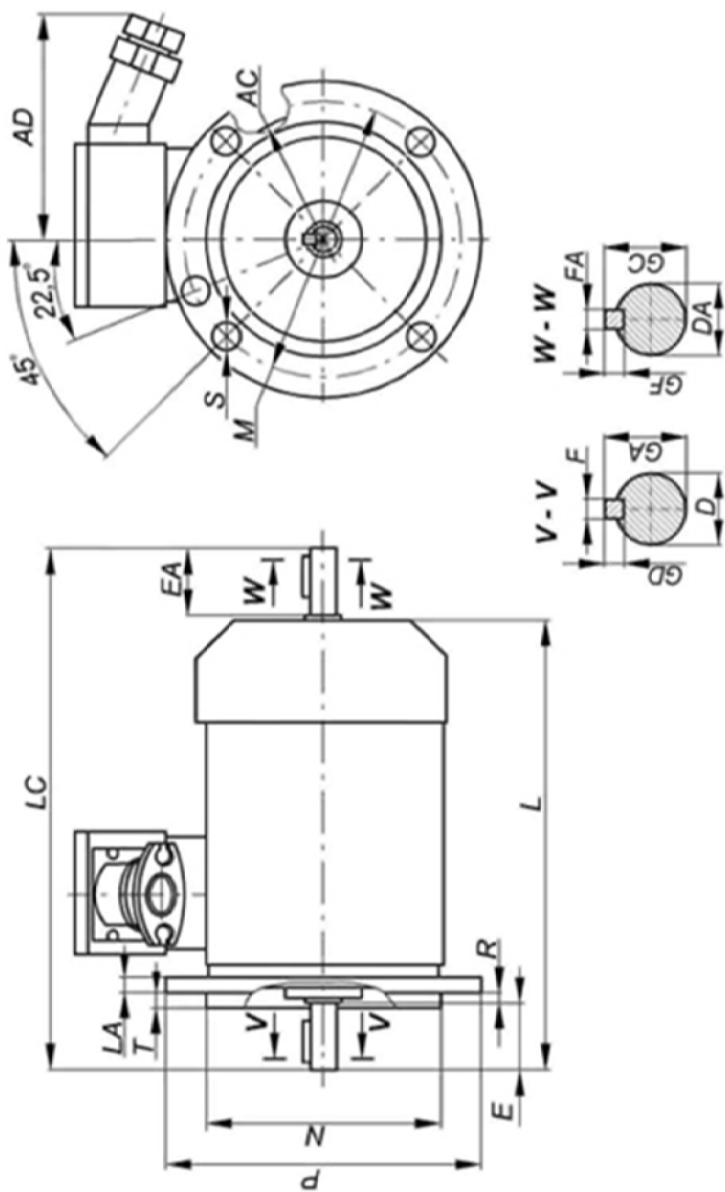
Габаритные, установочные и присоединительные размеры взрывозащищенных двигателей серии ВА. Монтажное исполнение [М 3...1, ПМ 3...2]
